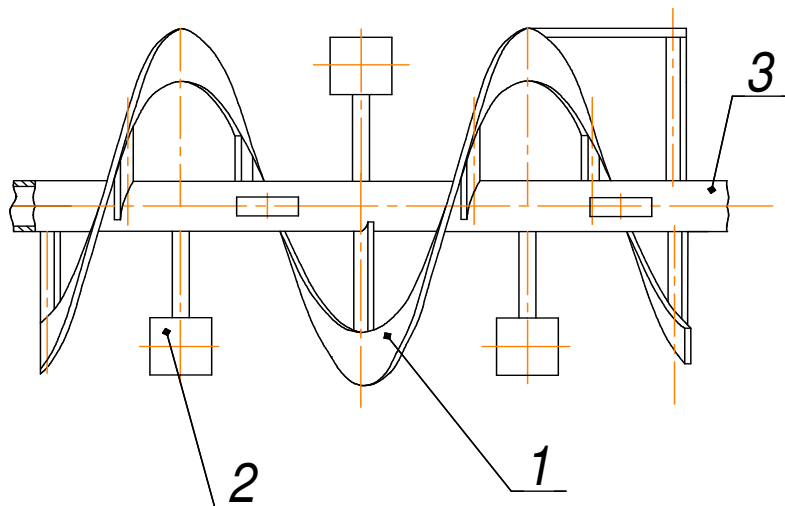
Схема робочого органа стрічково-лопатєвого змішувача:
